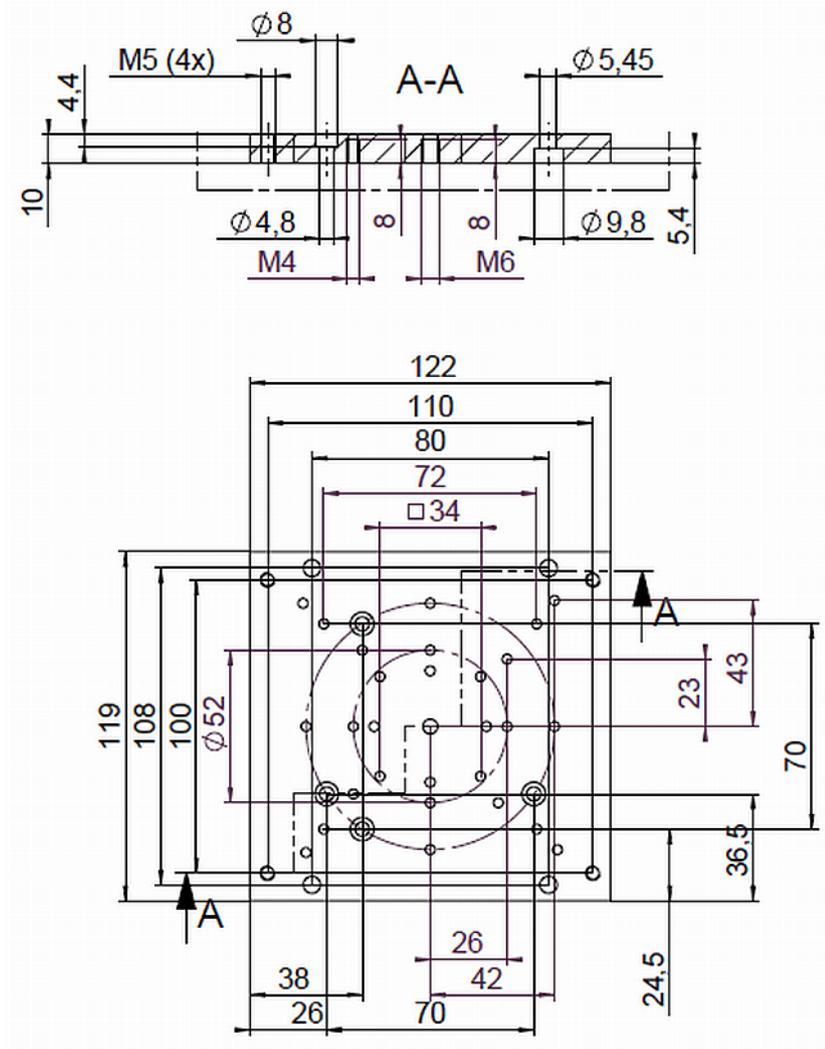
Abmessungen Montageadapter M-417.AP1
